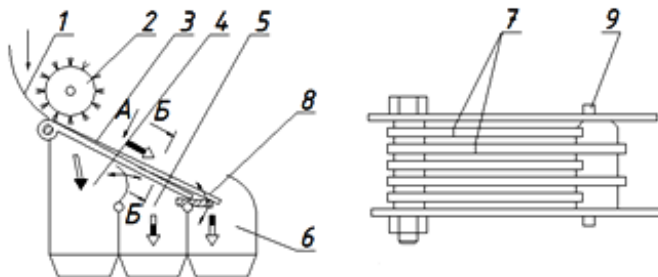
Решетний сепаратор: 1 – лоток; 2 – циліндрична щітка; 3 – решета; 4, 5, 6 – приймальники розділених фракцій; 7– пластини; 8 – вісь
